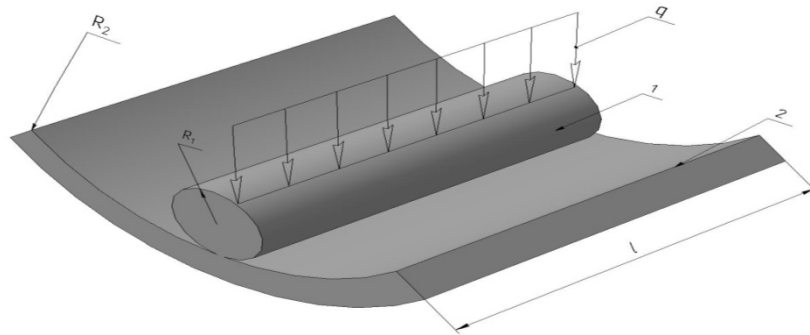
Базова розрахункова схема ролика та бігової доріжки
